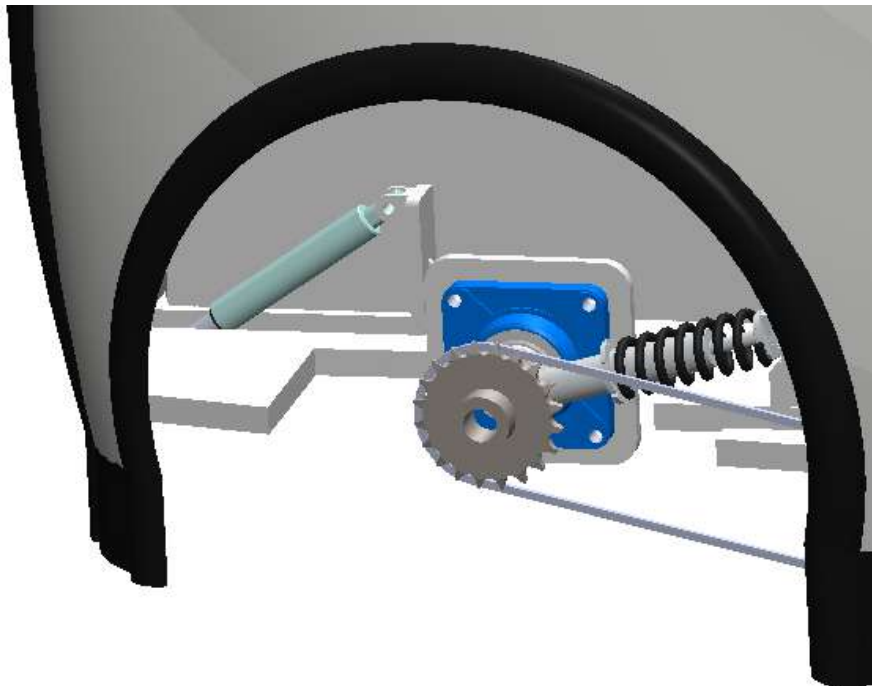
Sistema de apertura de puerta inferior con pistón de elevación. Fuente: (Vaca, José, 2018)
